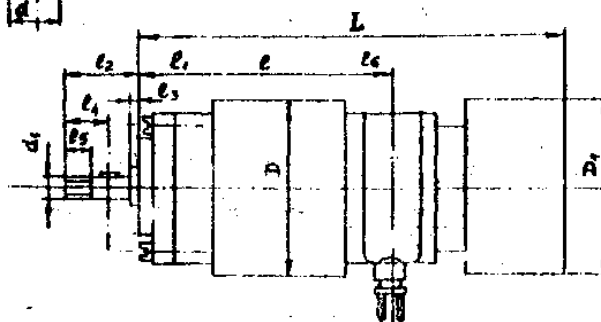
Конструктивные размеры двигателей серии ДПМ
